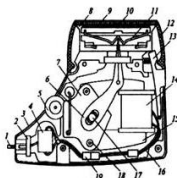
Электробритва «Чайка-304-авто» (разъемный полукорпус): 1 – штекер; 2 – колодка; 3 – полукорпус; 4 – конденсатор; 5 – пускатель; 6 – кулиса; 7 – пластина; 8 – неподвижный нож; 9 – съемный нож; 10 – подвижный нож; 11 – пружина; 12 – волосоулавливатель; 13 – фиксатор; 14 – катушка; 15 – сердечник статора; 16 – провода; 17 – эксцентриковая втулка; 18 – букса; 19 – хрорвиниловая втулка.
